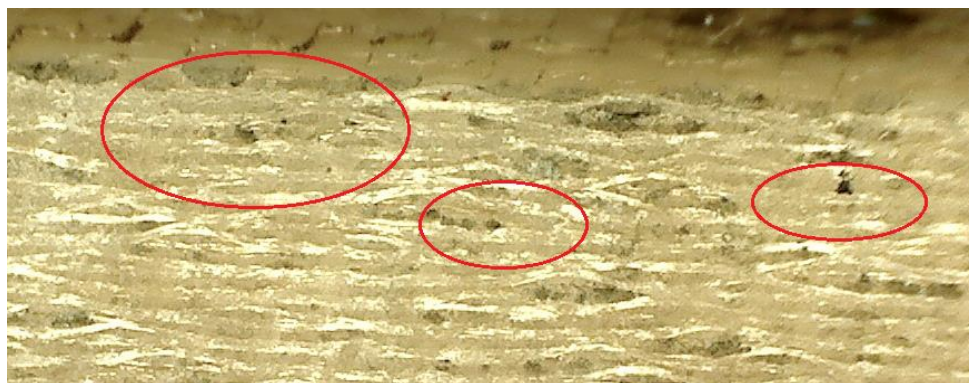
Обработанная поверхность заготовки из стеклопластика жестким шлифовальным кругом 14AF60G7
